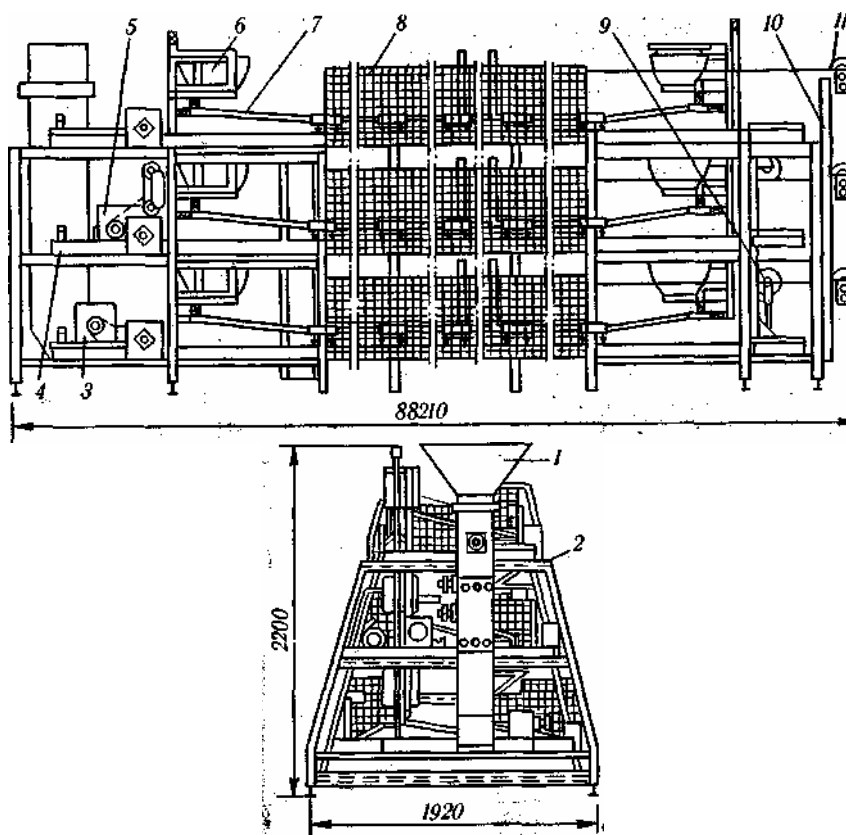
Схема кліткової батареї БКМ-ЗБ: 1 – бункер-дозатор; 2 – передній стояк; 3 – привід кормороздавача; 4 – кормовий жолоб; 5 – привід скребків для видалення посліду; 6 – бачок-вирівнювач; 7 – лінія напувалок; 8 – клітки; 9 – механізм натягування троса скребка; 10 – задній стояк; 11 – лебідка для підймання напувалок.
